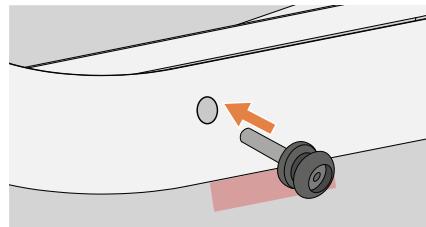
Befestigen der Schraube mit Schlaufenverbindung.
